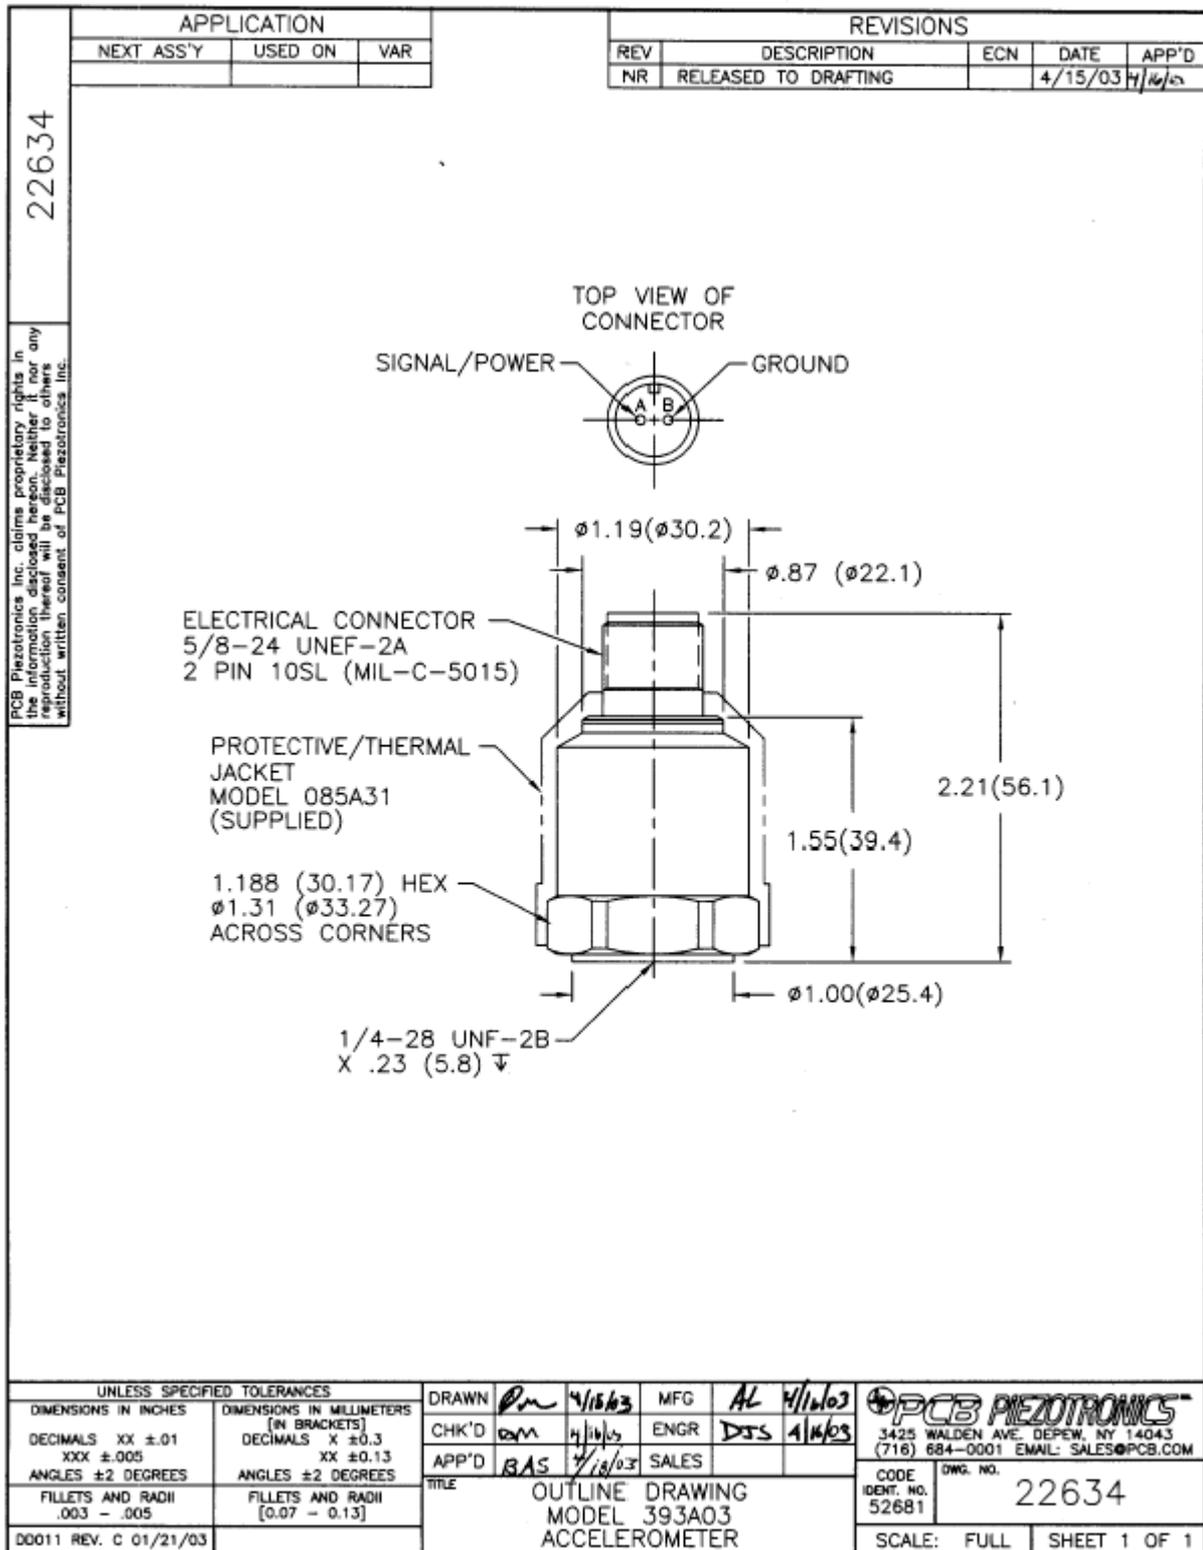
Rappresentazione sezione accelerometri e pianta connettore
